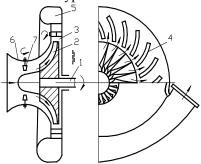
Схема центробежного компрессора: 7 – вал; 2 – рабочее колесо; 3 – диффузор; 4 – лопатка; 5 – воздухосборник; 6 – входное устройство; 7 – вращающийся направляющий аппарат
